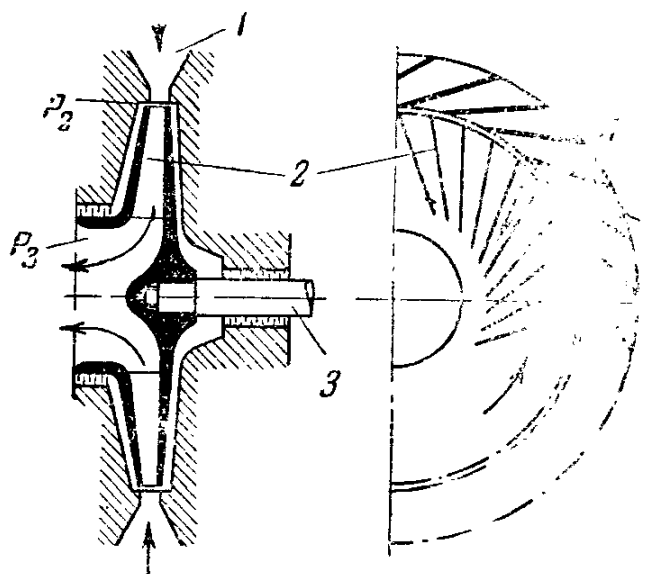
Схема рабочего колеса турбодетандера реактивного типа:
